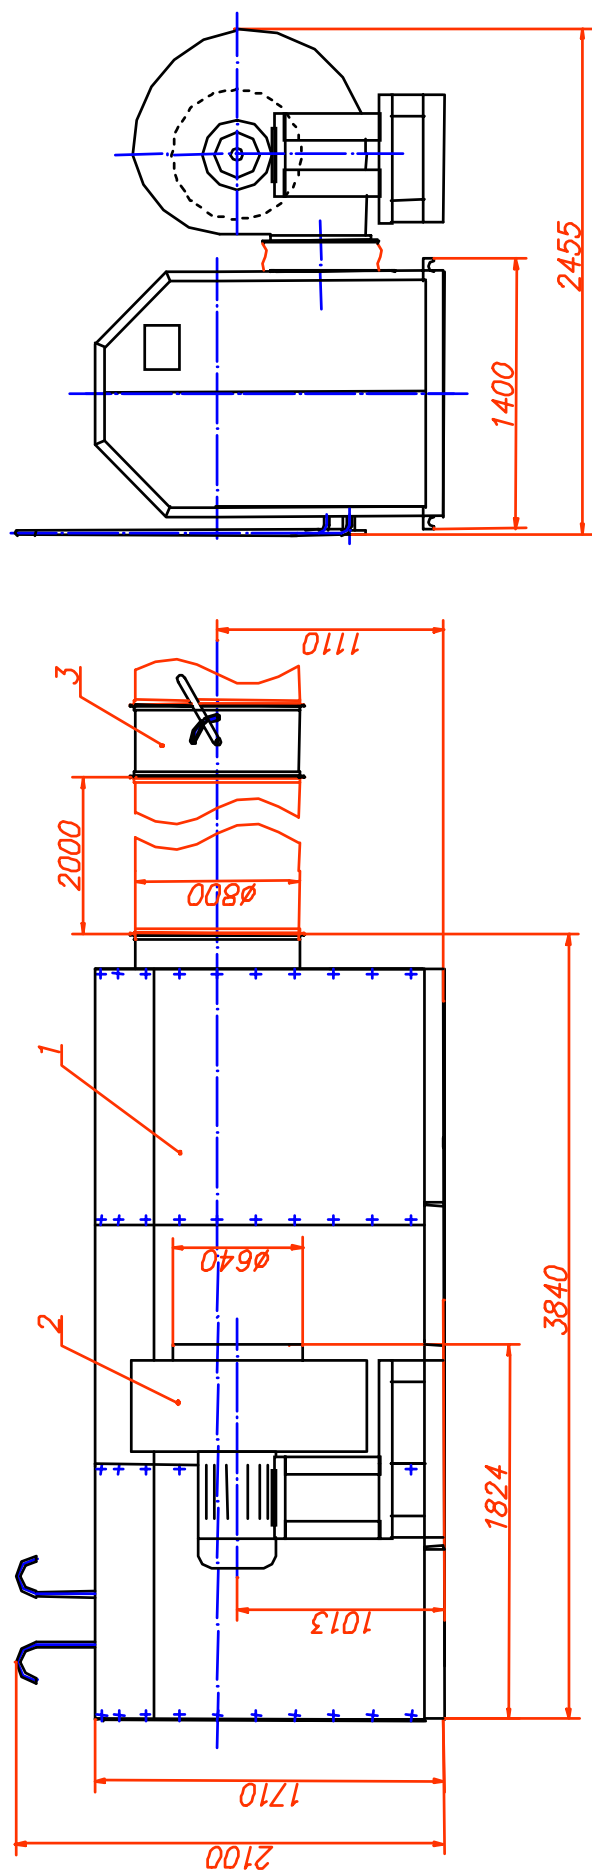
Теплогенератор Т1000G, габаритные и присоединительные размеры
